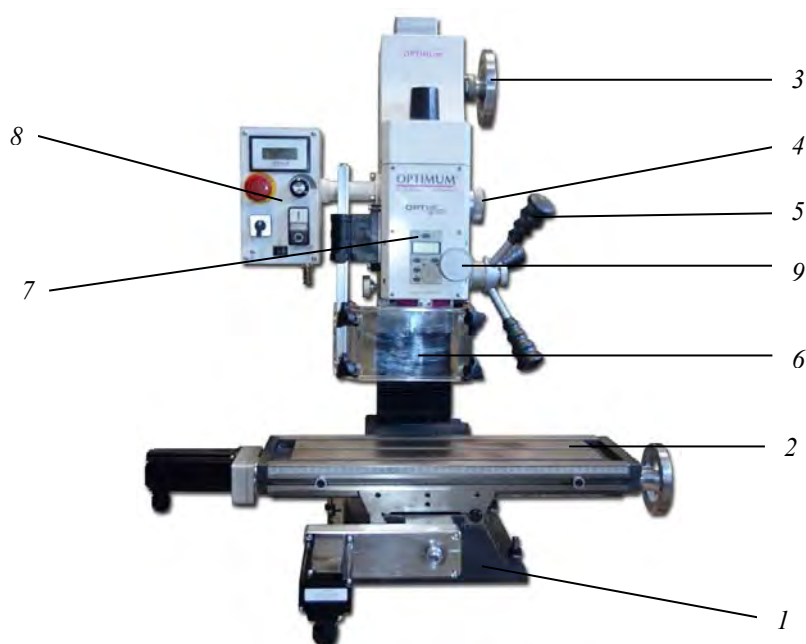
Общий вид фрезерного станка модели Optimum BF20 Vario
